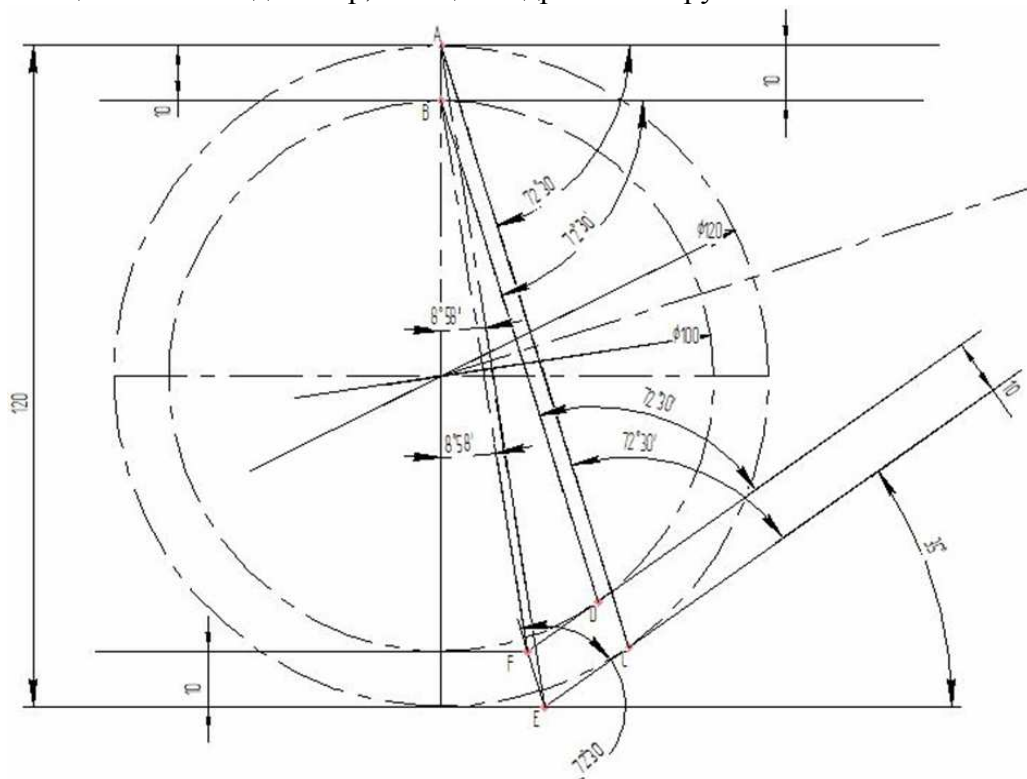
Геометрия разделки конической обечайки и трубы перед сваркой
